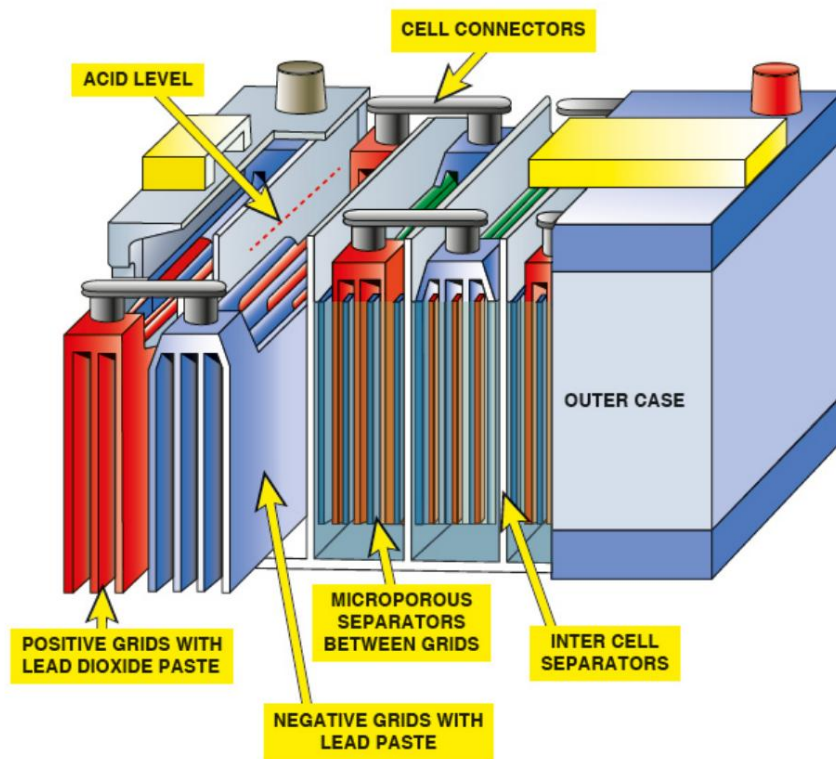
Las baterías están construidas con placas agrupadas en celdas e instaladas en una caja de plástico.
